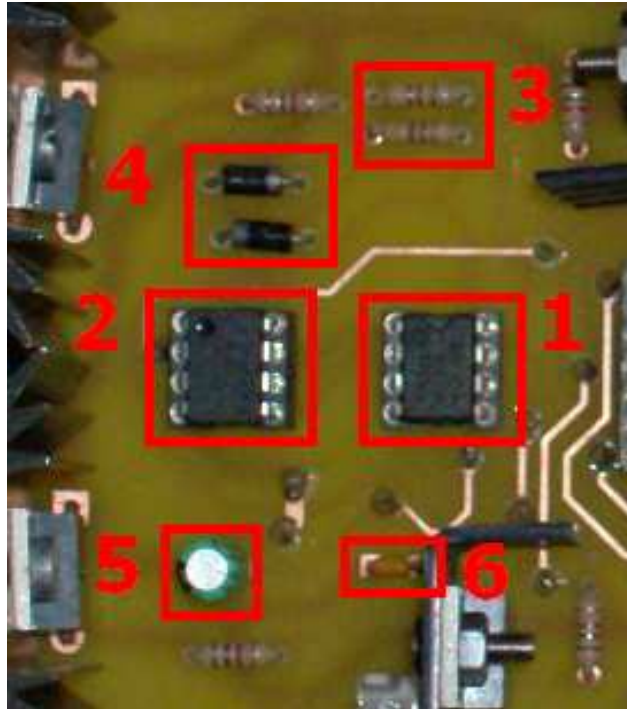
Vista en grande de la disposición del integrado LM555 y componentes pasivos en la placa PCB
